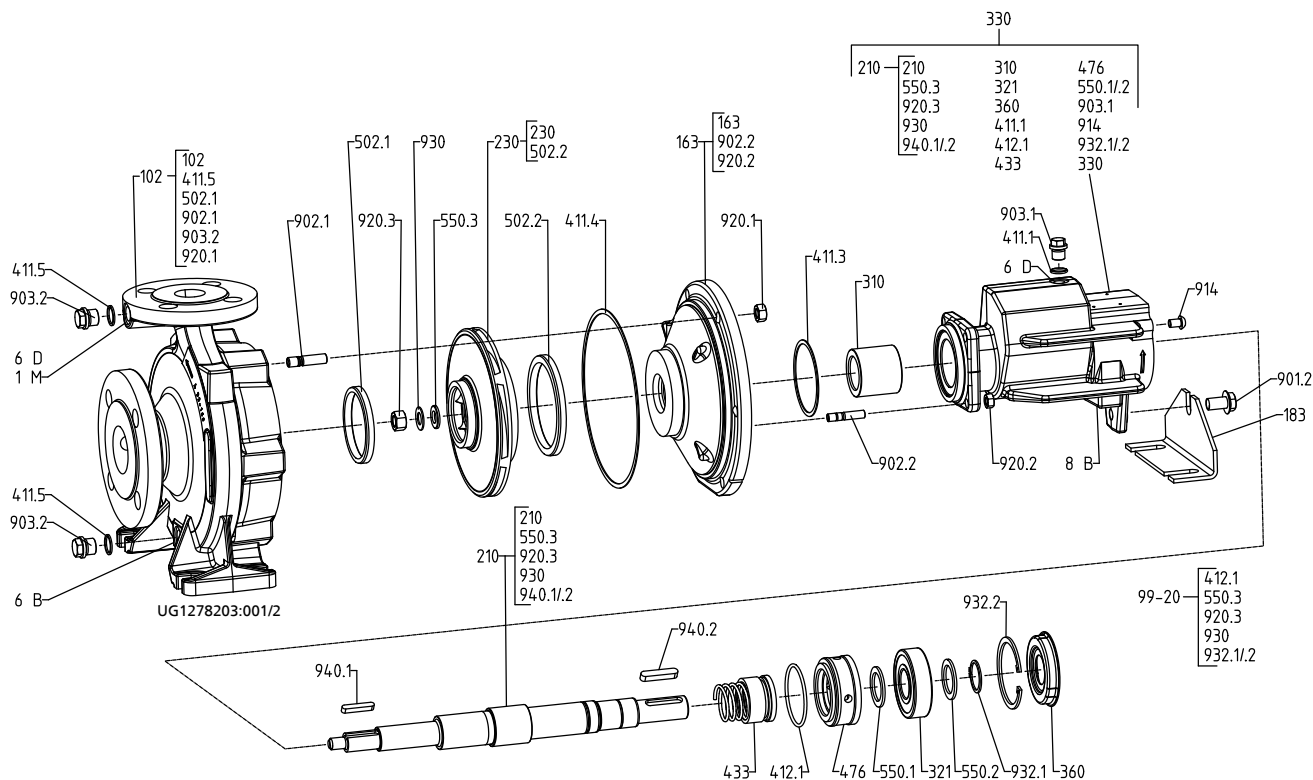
Детализированный чертеж Etanorm SYT, WE 25
